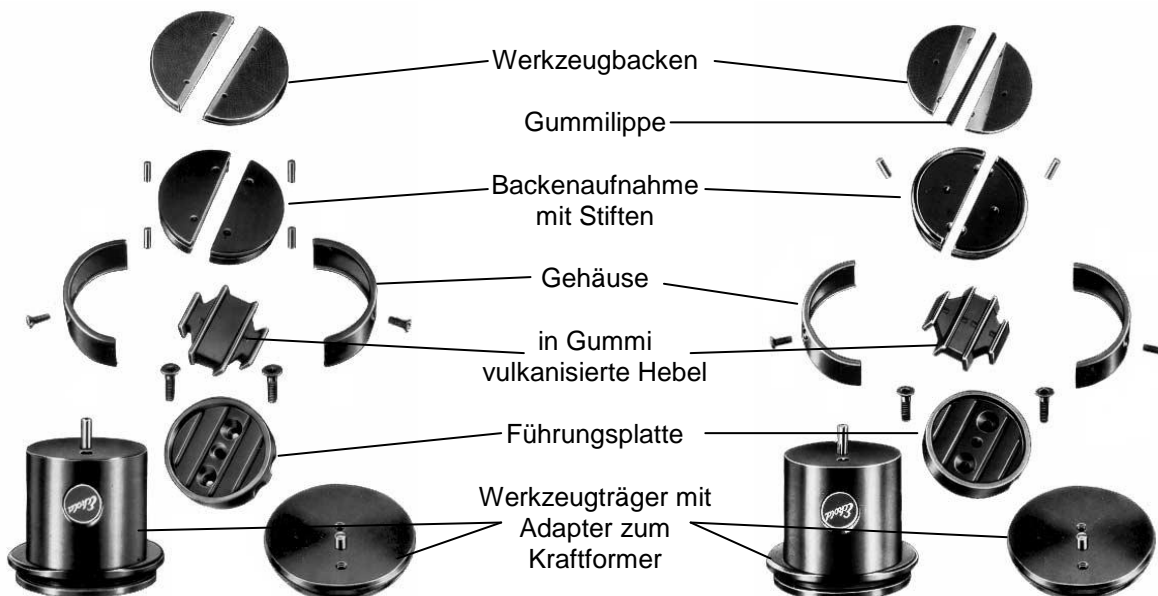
Aufbau der Umformwerkzeuge (l. Strecken, r. Stauchen) [Q.: Eckold]
